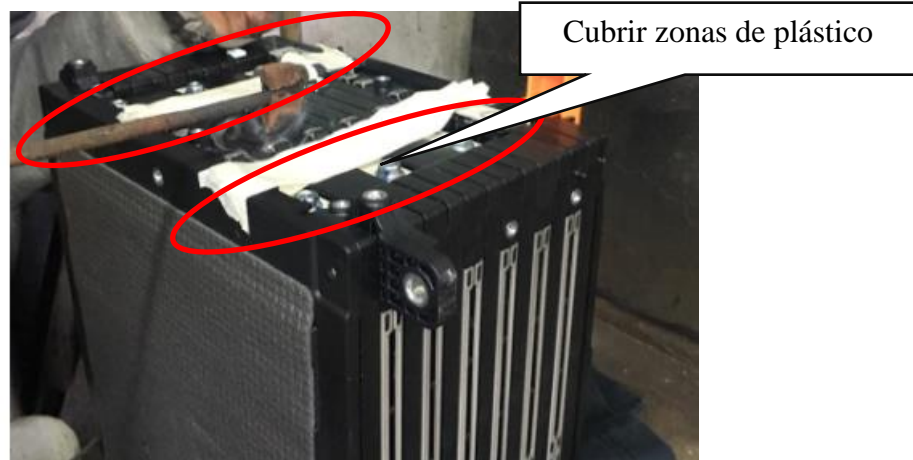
Soldadura de placa. Fuente: Autores.
